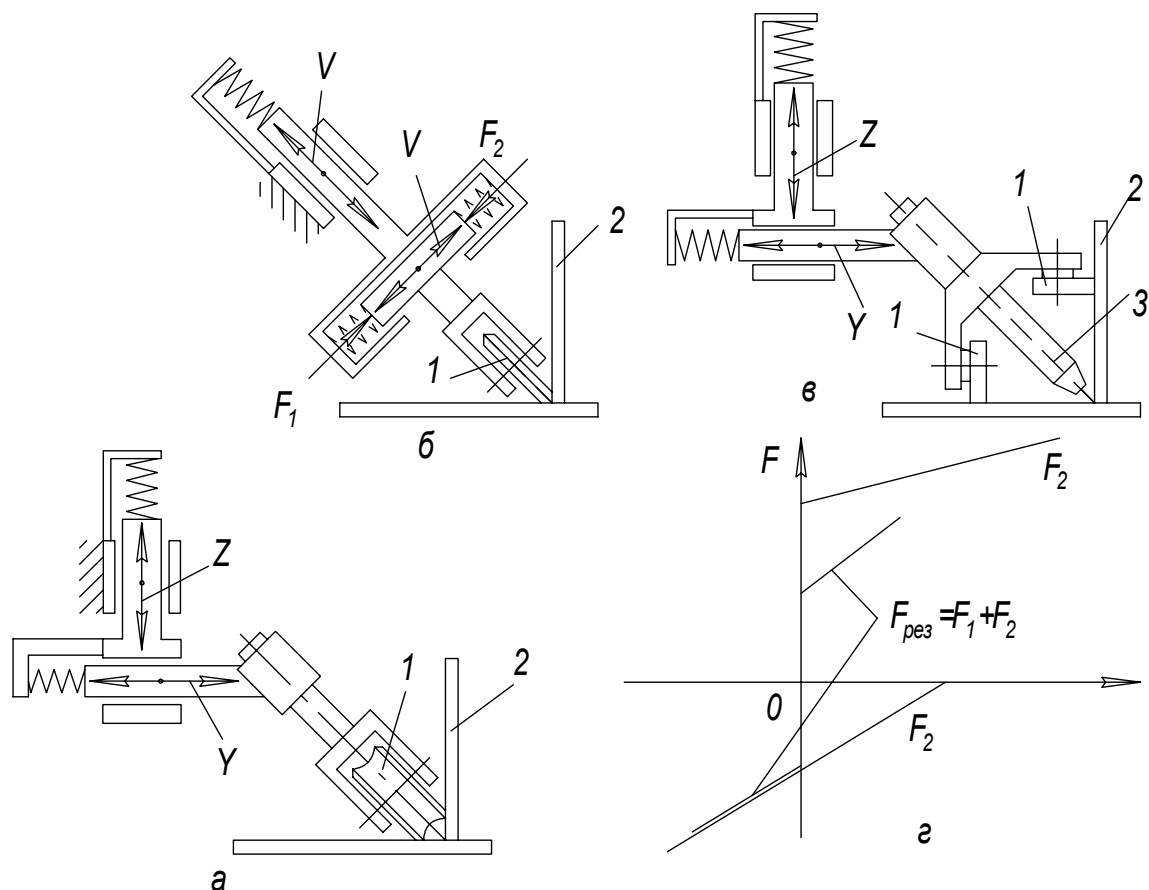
Схеми двокоординатних пристроїв прямої дії для зварювання кутових швів:
